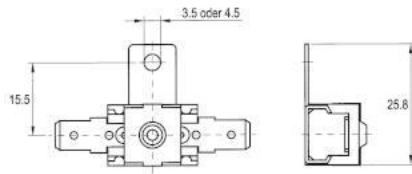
Flansch mit einseitigem Befestigungsflappen
